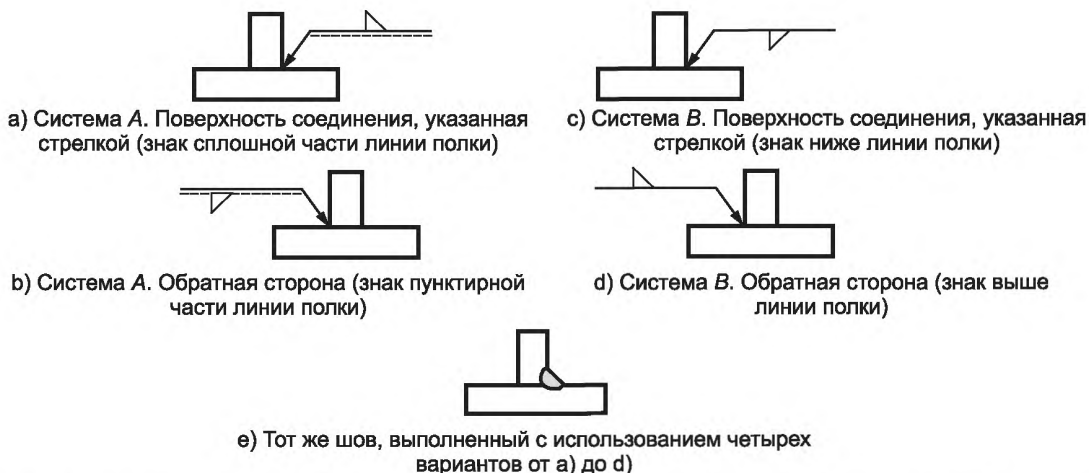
Примеры обозначений сварного соединения для поверхности соединения указанной стрелкой и обратной стороны
